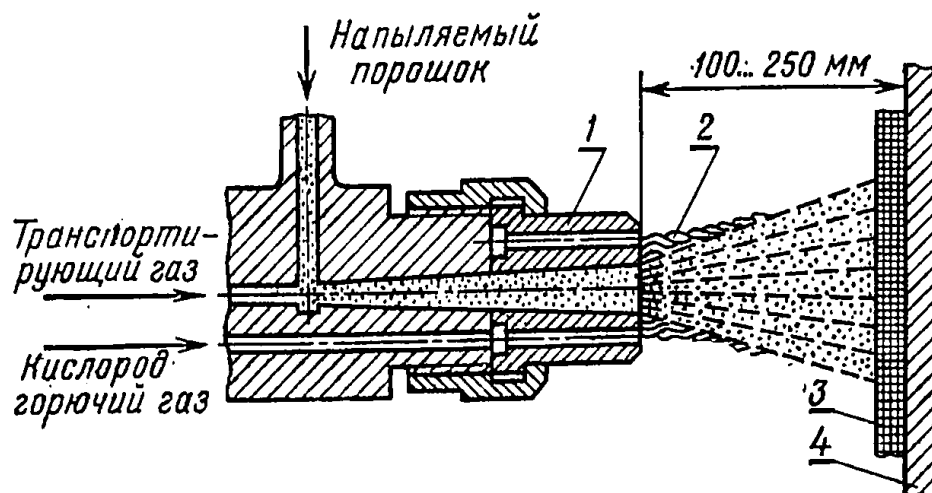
Ввод порошка при помощи транспортирующего газа:
